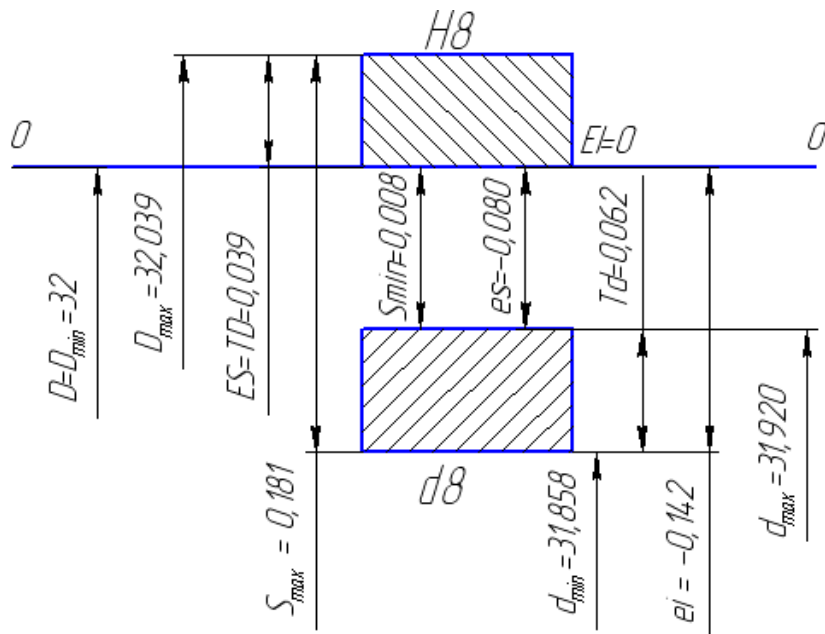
Схема розташування полів допусків посадки із зазором
